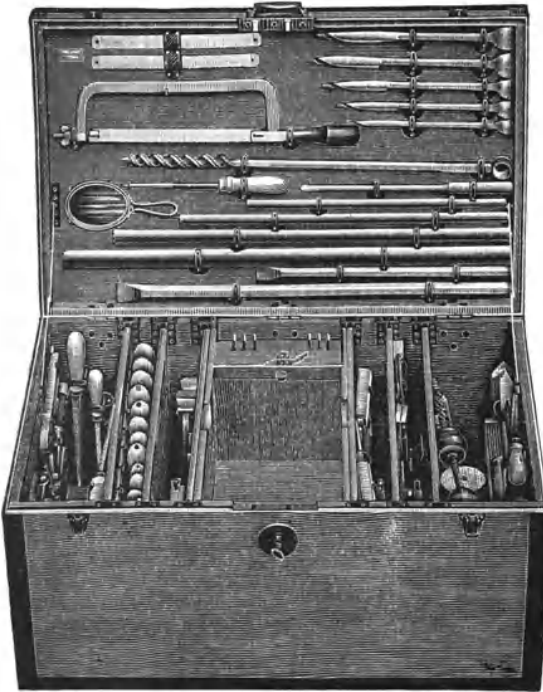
Werkzeugkoffer für elektrische Montagen;
